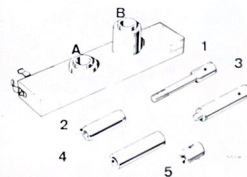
Útiles para la extracción y reposición de un bulón de pistón, de un motor tipo 813.
